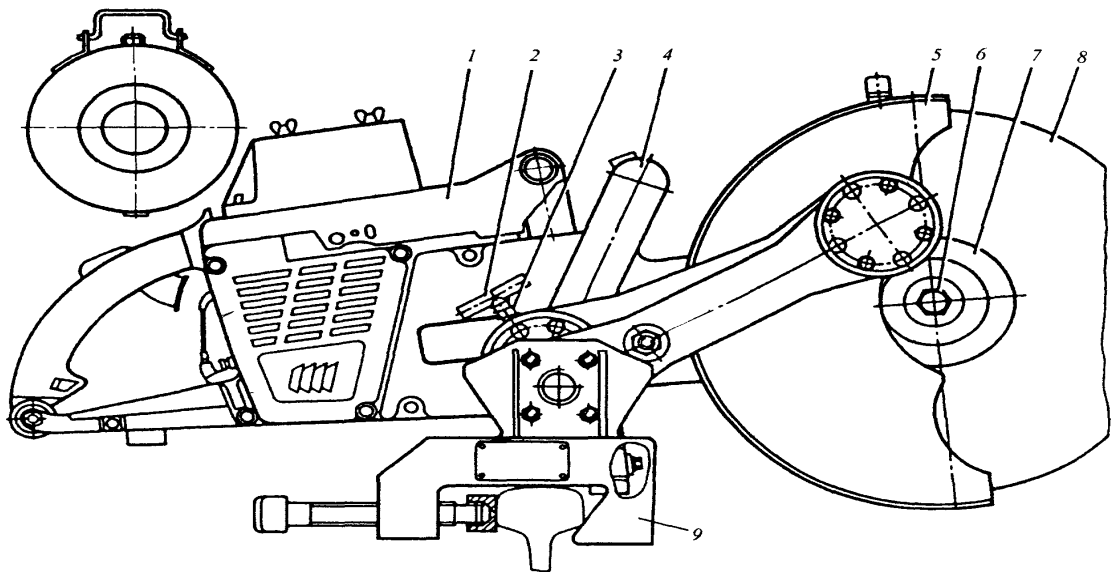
Станок рельсорезный РР80: 1-двигатель; 2-винт; 3-пружина; 4-кронштейн; 5-защитный кожух; 6-болт; 7-нажимная шайба; 8-отрезной круг; 9 – направляющая рама
